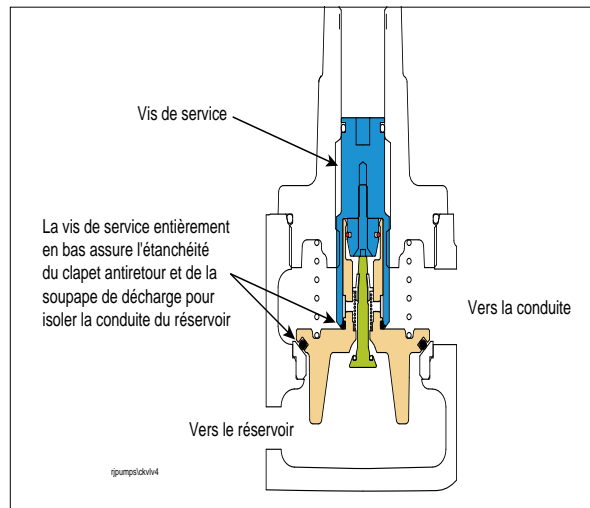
Blocage du clapet antiretour pour tester la conduite
